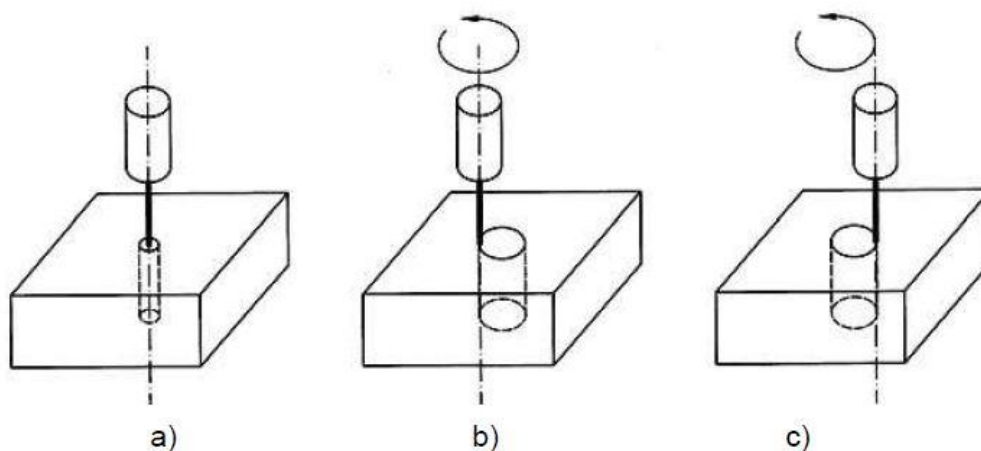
Ukázka soustružení pískovce AWJ.[23]
